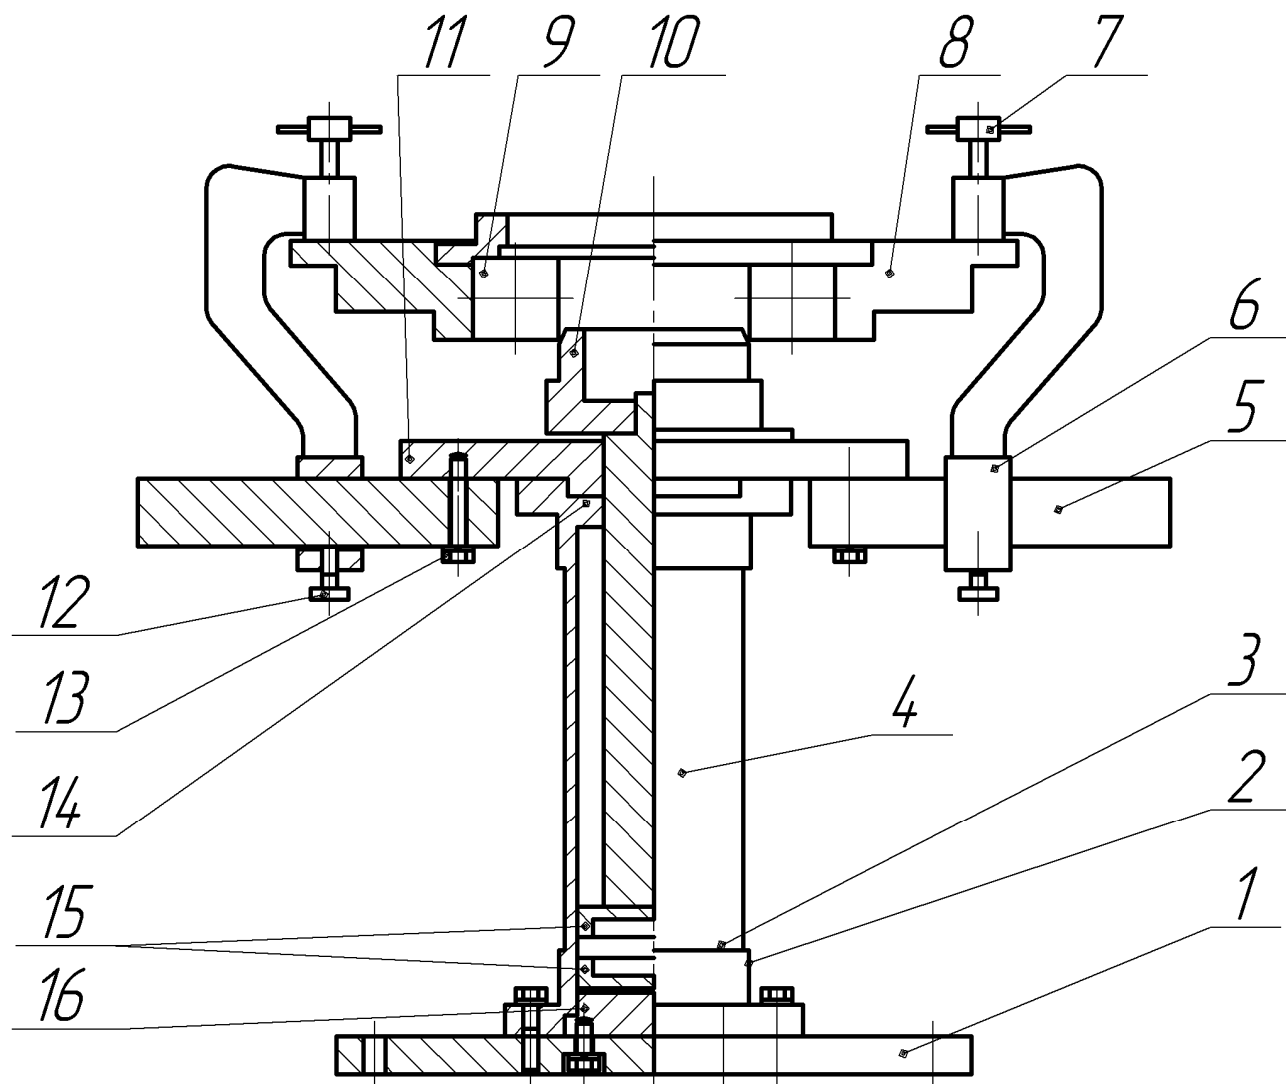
Пресовий стенд для виїмки підшипників з підшипникового щита
